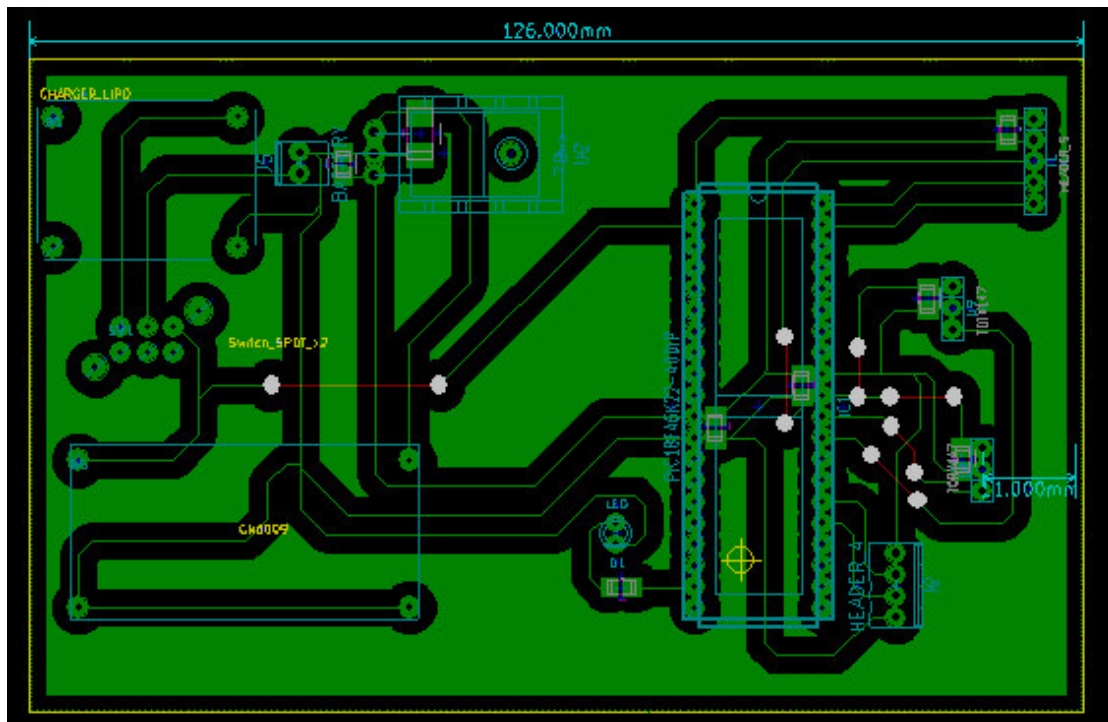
Diseño PCB de la tarjeta del módulo remoto de control
